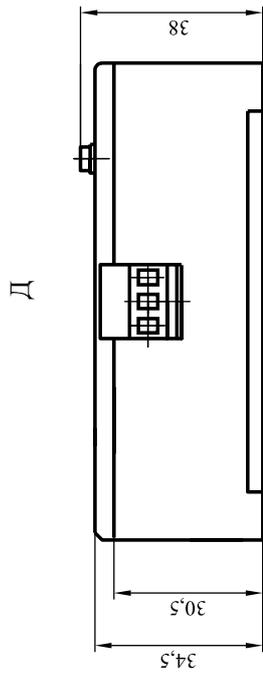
Габаритно-установочные размеры генератора-преобразователя ВП-10-6,0-125-Д
